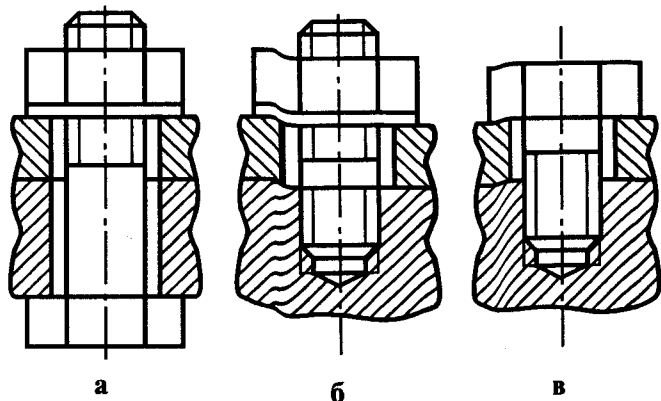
Резьбовые соединения при помощи: а — болта; б — шпильки; в — винта
